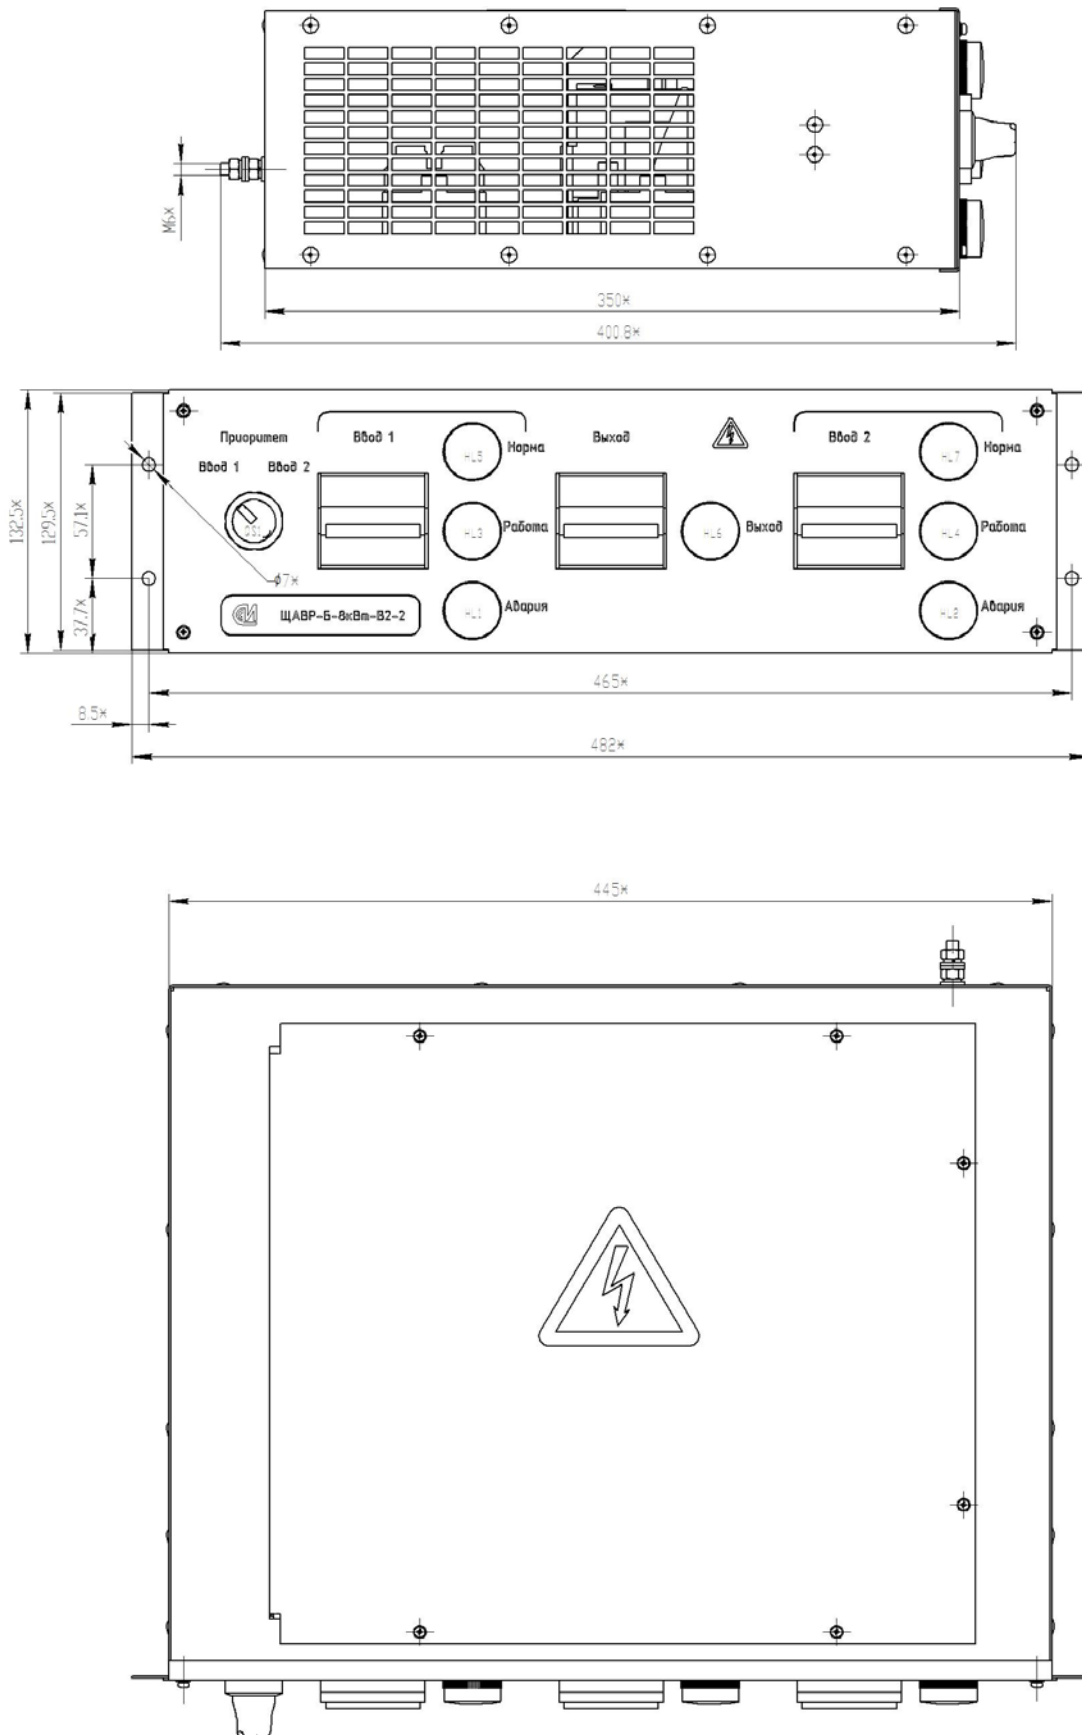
Габаритно-присоединительные размеры щита автоматического включения резерва ЩАВР-Б-8кВт-В2-2.
